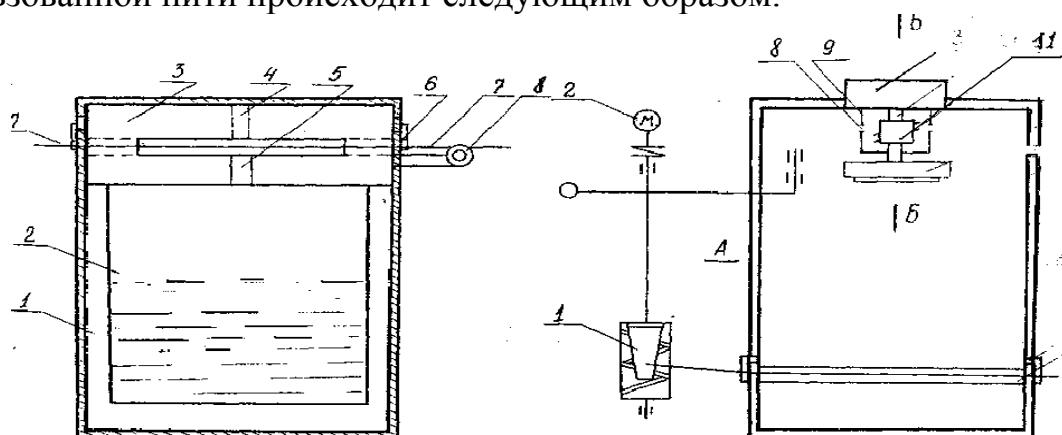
Схема устройства для снятия извитости повторно используемой нити
